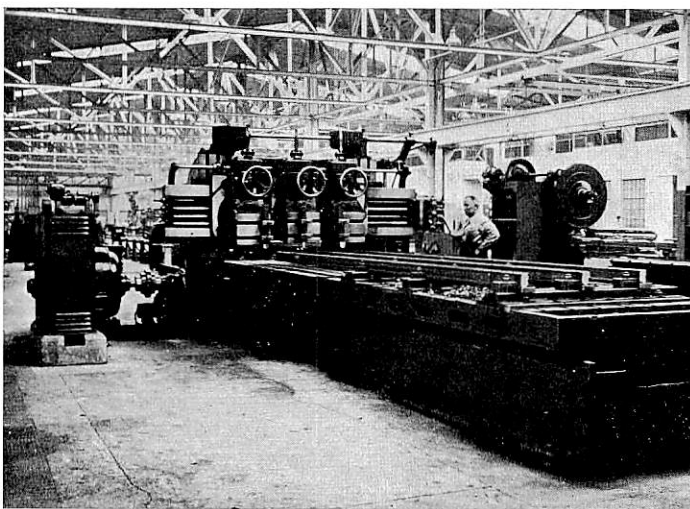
Zungenhobelmaschine mit Gleichstrom-Umsteuermotor.
